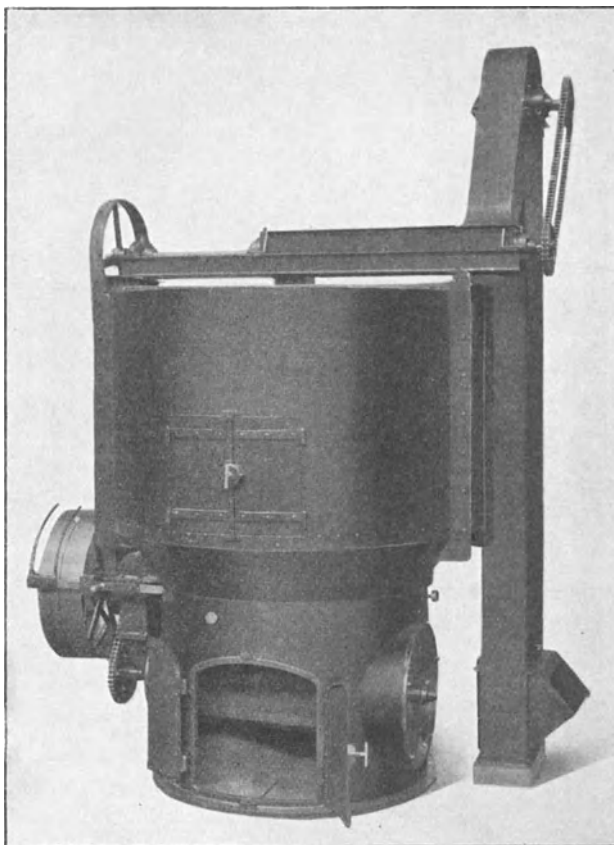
Kollergang mit eingebautem Trommelsieb.
